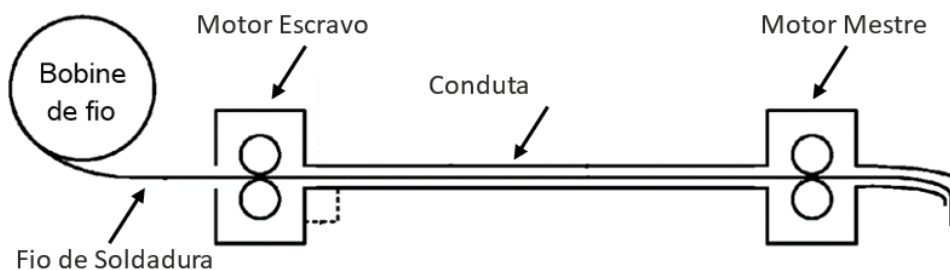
Alimentação do fio de soldadura ideal [61]
